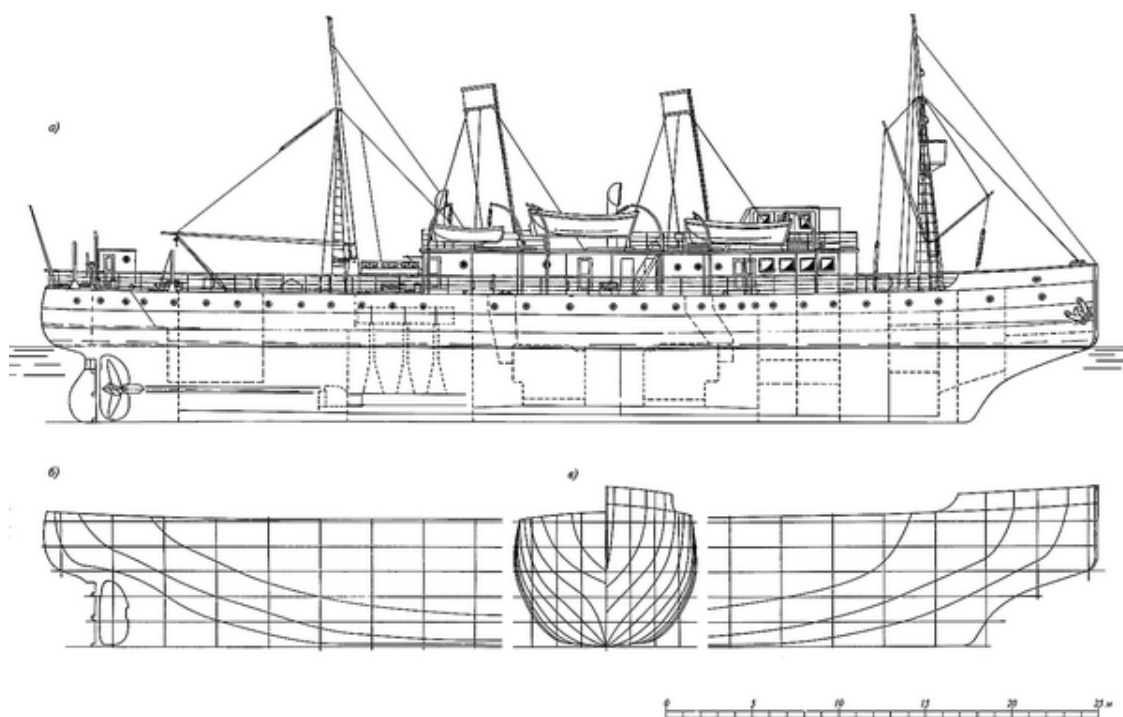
Чертежи «Ангара»: а) вид сбоку; б) теоретический чертеж (проекция «бок» и «корпус»)
